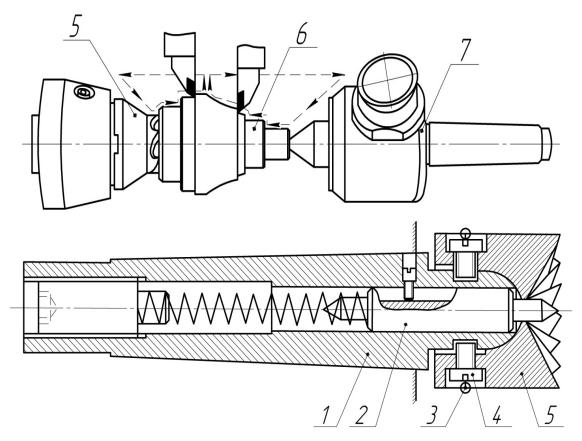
Поводковый зубчатый патрон: 1 — корпус; 2 — плавающий центр; 3 — прижимное кольцо; 4 — винт; 5 — зубчатый поводок; 6 — заготовка; 7 — вращающийся центр
